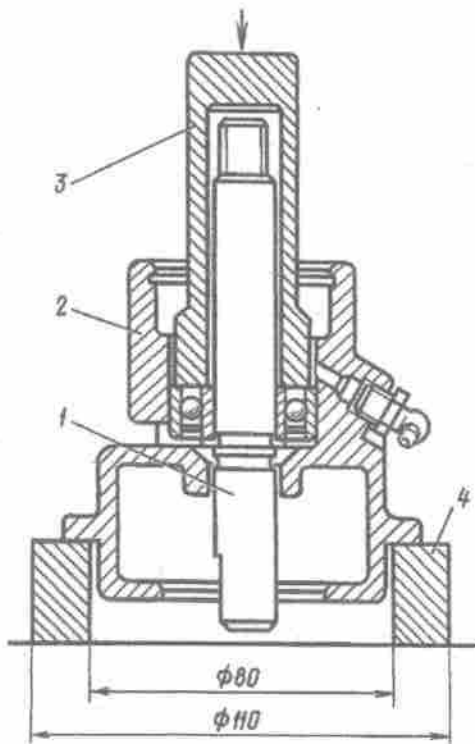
Einpressen der Welle nebst Lager ins Gehäuse der Wasserpumpe:
